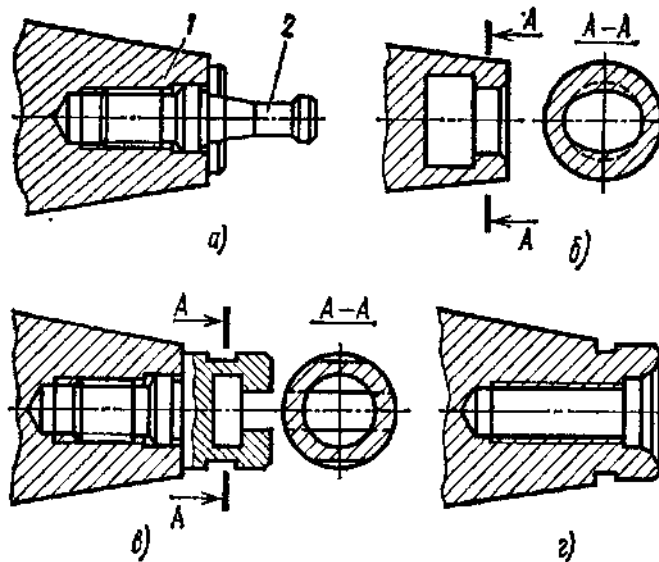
Захоплювальні пристрої інструментальних оправок
